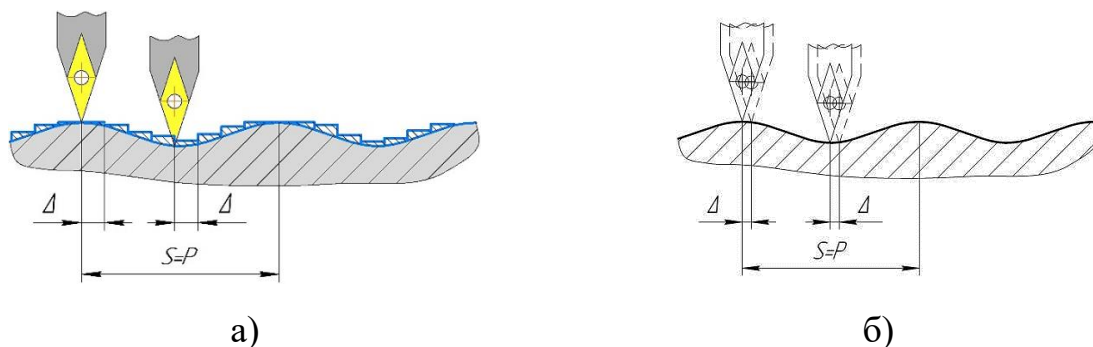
Схема зрізання припуску при точінні внутрішніх різей стандартним різцем: а) чорнова обробка; б) чистова обробка
